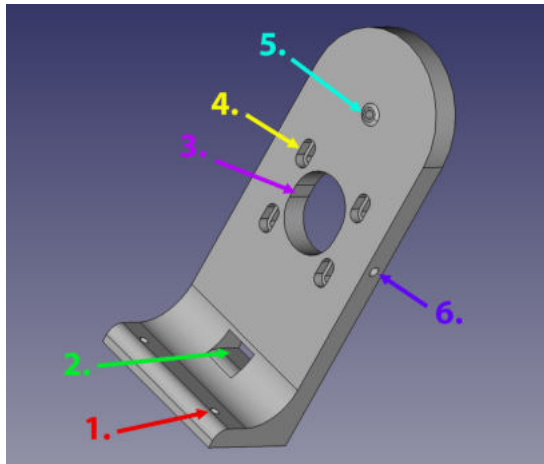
Rechte Befestigung der Kamerahalterung. Löcher für Befestigung an Hauptplattform (1.). Loch um Kabel des Motors für die Tilt-Bewegung hindurch zu führen (2.). Langgezogenes Loch um Motorpin mit Zahnrad hindurch zu stecken (3.). Vier Langgezogene Löcher für die höhenverstellbare Befestigung des Motors (4.). Leichte Erhebung mit Loch um Kamerahalterung mit Zahnrad am Fuß zu befestigen und das Zahnrad bei Drehung nicht überall am Fuß Kontakt hat (5.). Seitliches Loch um Zahnrad an montiertem Motor festzuschrauben (6.).
